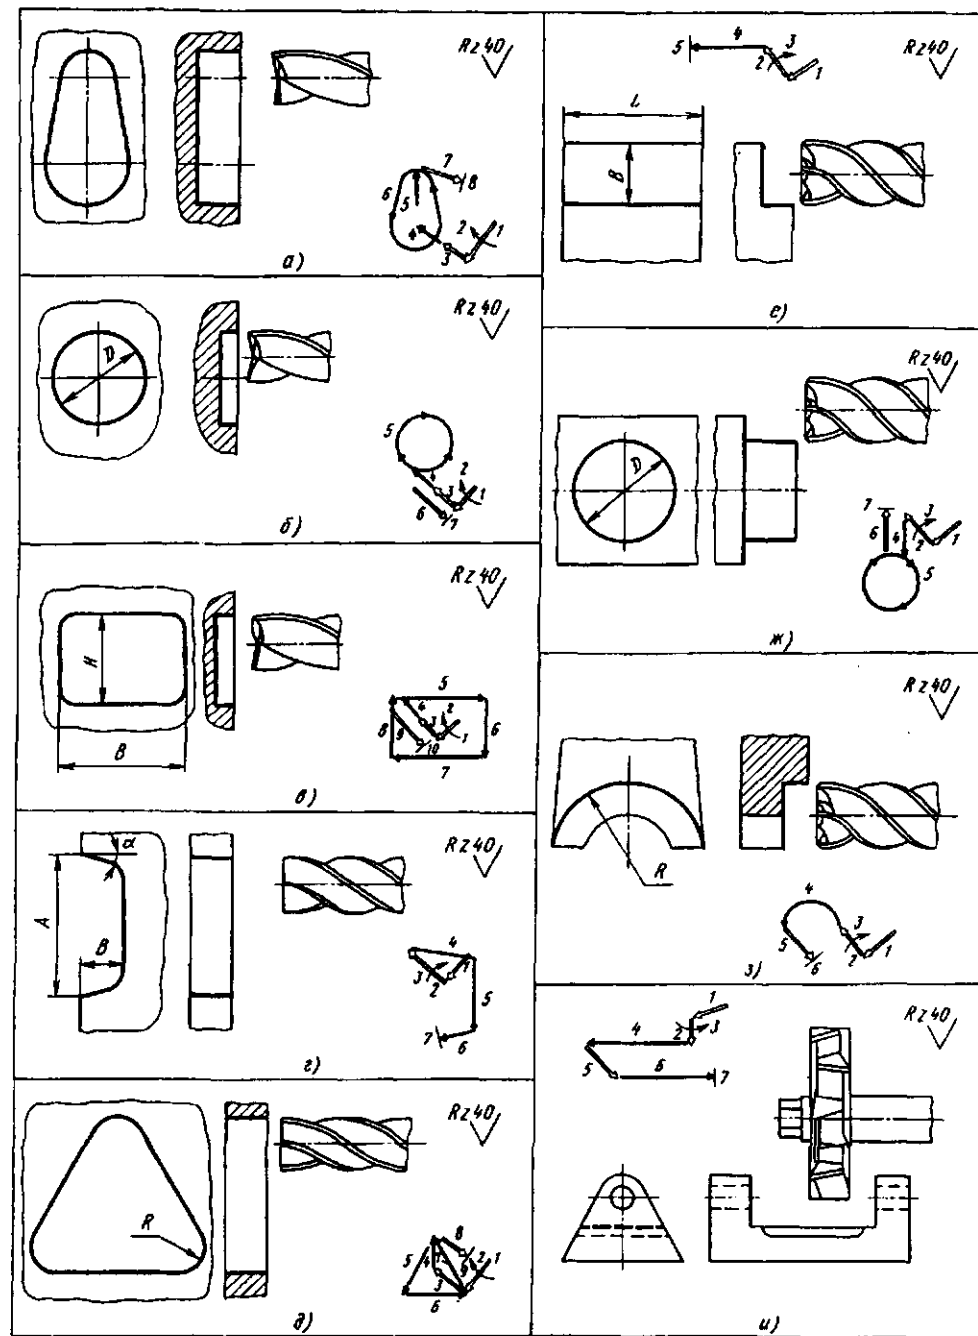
Типовые циклы контурного фрезерования: а – д – карманов и окон шпоночными и концевыми фрезами; е – з – уступов, бобышек концевыми фрезами; и – уступа дисковой трехсторонней фрезой
